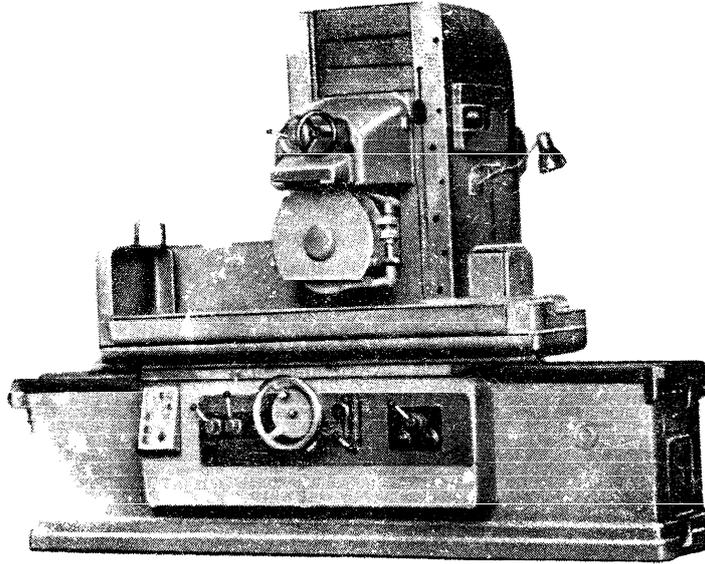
Плоскошлифовальный станок модели ЗБ722
